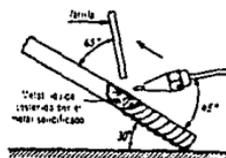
Esquema de una soldadura oxiacetilénica en semimontante.
